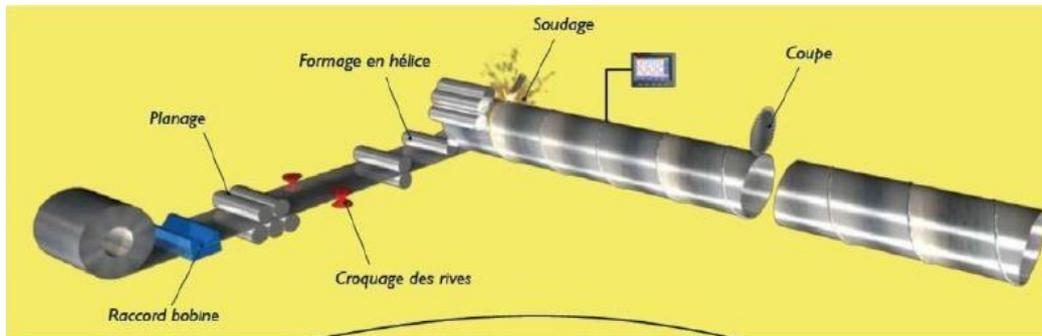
Principe de fabrication des tubes soudés en spirale.
